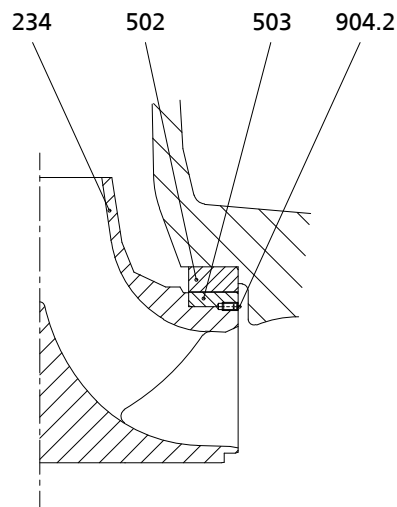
Деталировочный чертеж: Рабочее колесо с вращающимся кольцом
